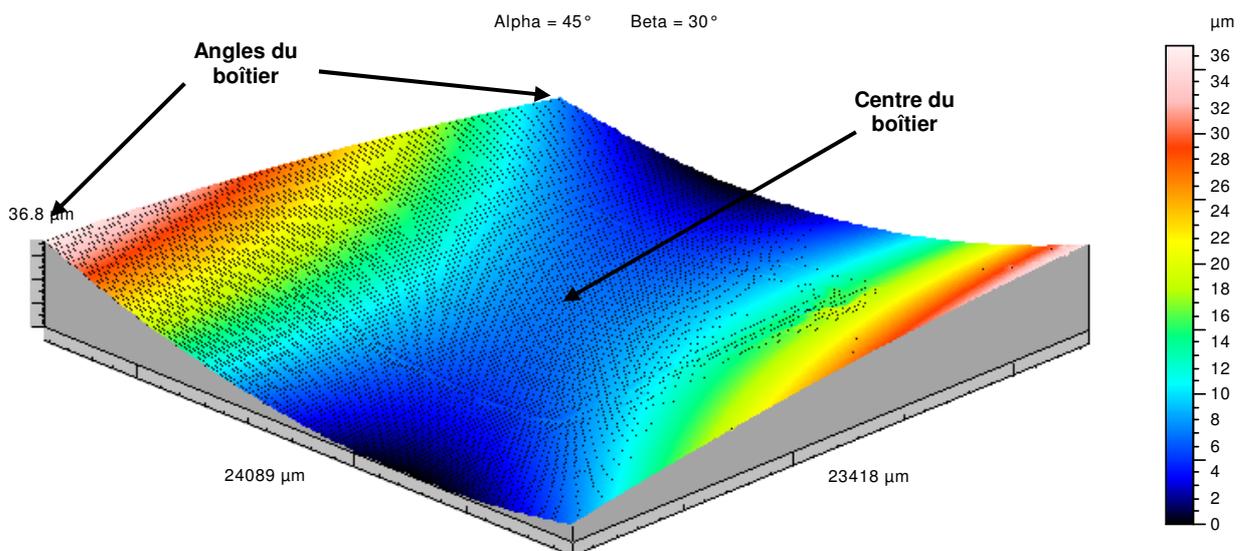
Cartographie en 3 dimensions de la surface du boîtier, après assemblage du BGA
